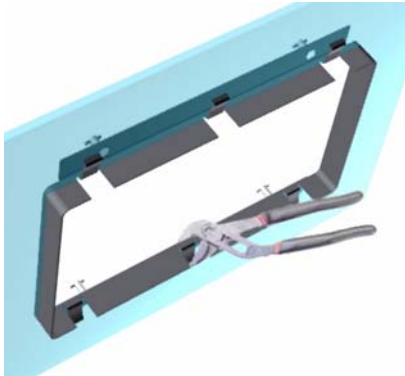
Rahmen der Klammer für die Paneelmontage
